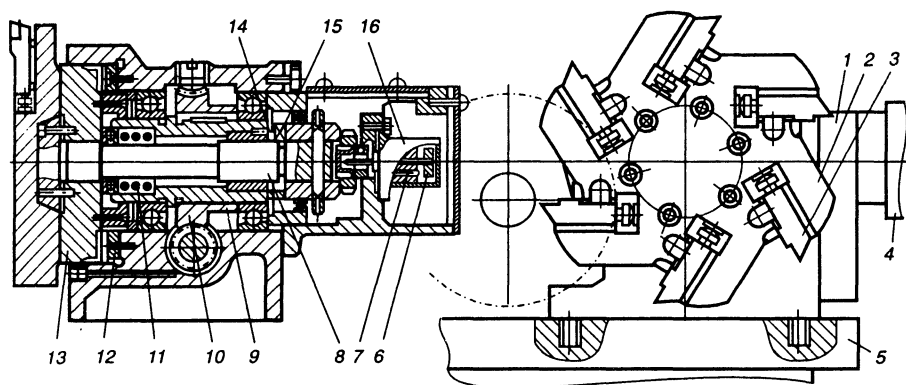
Шестипозиционный резцедержатель токарного станка 16К20ФЗС5
